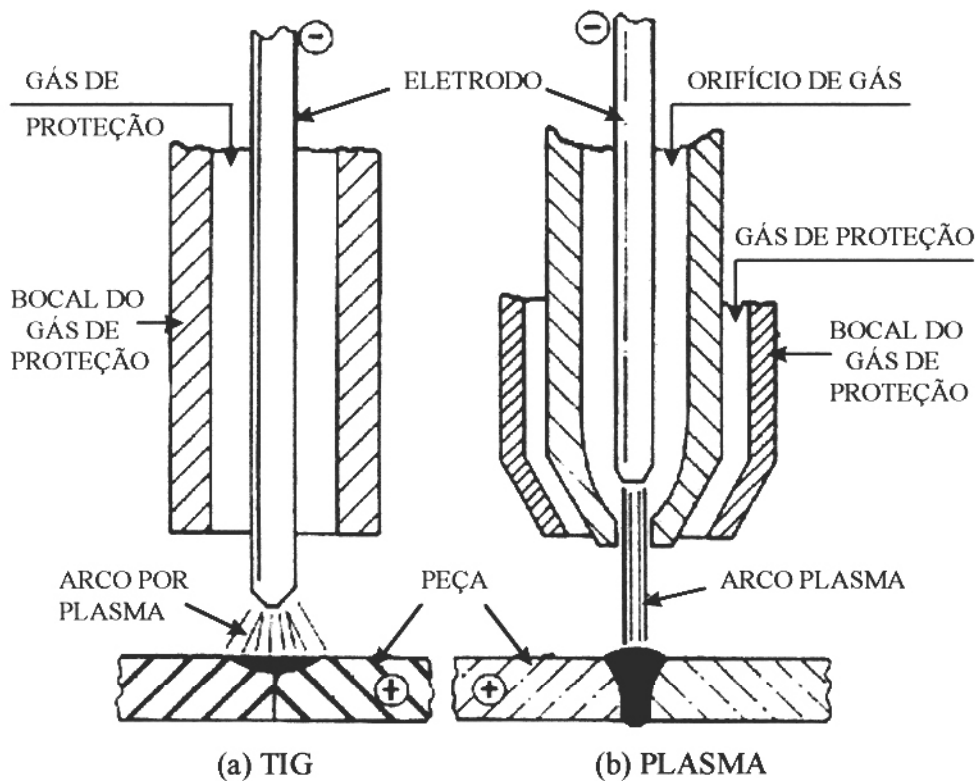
Comparação entre os processos de soldagem: (a) TIG e (b) Arco Plasma.
